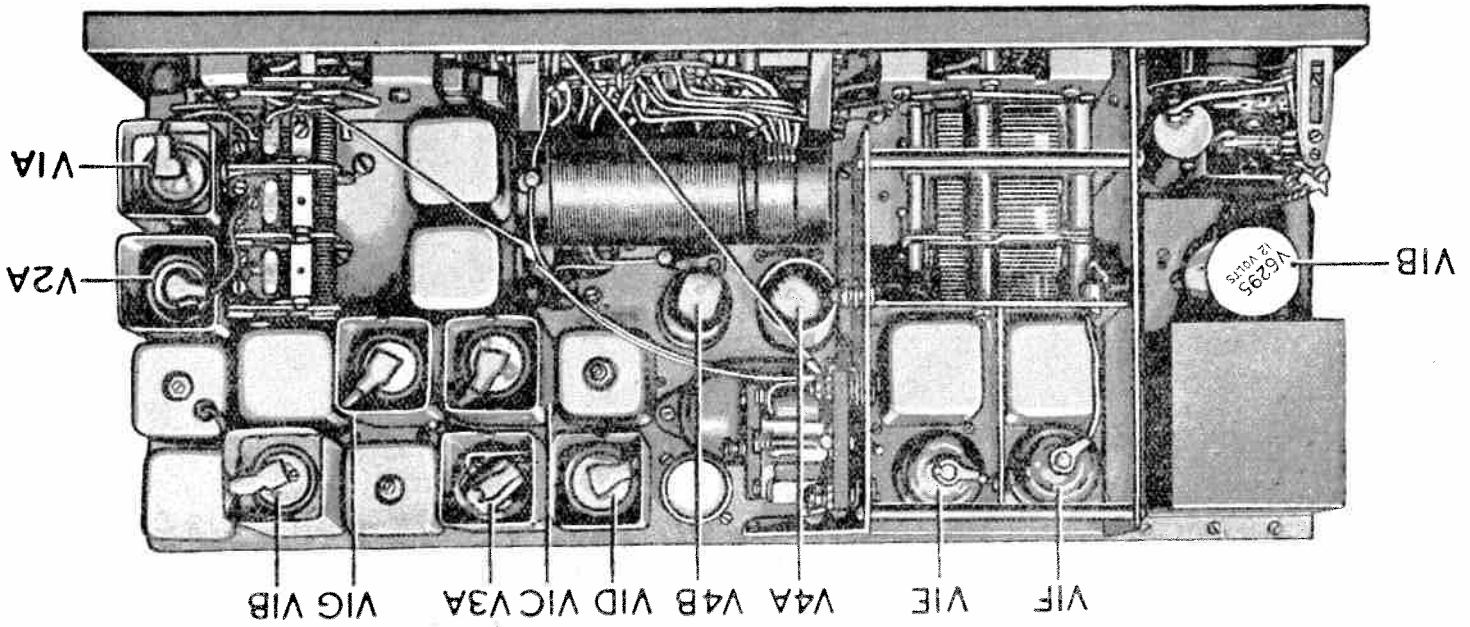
POSTE RADIO N° ZC.1MK II. VUE DU CHASSIS PAR EN DESSUS
